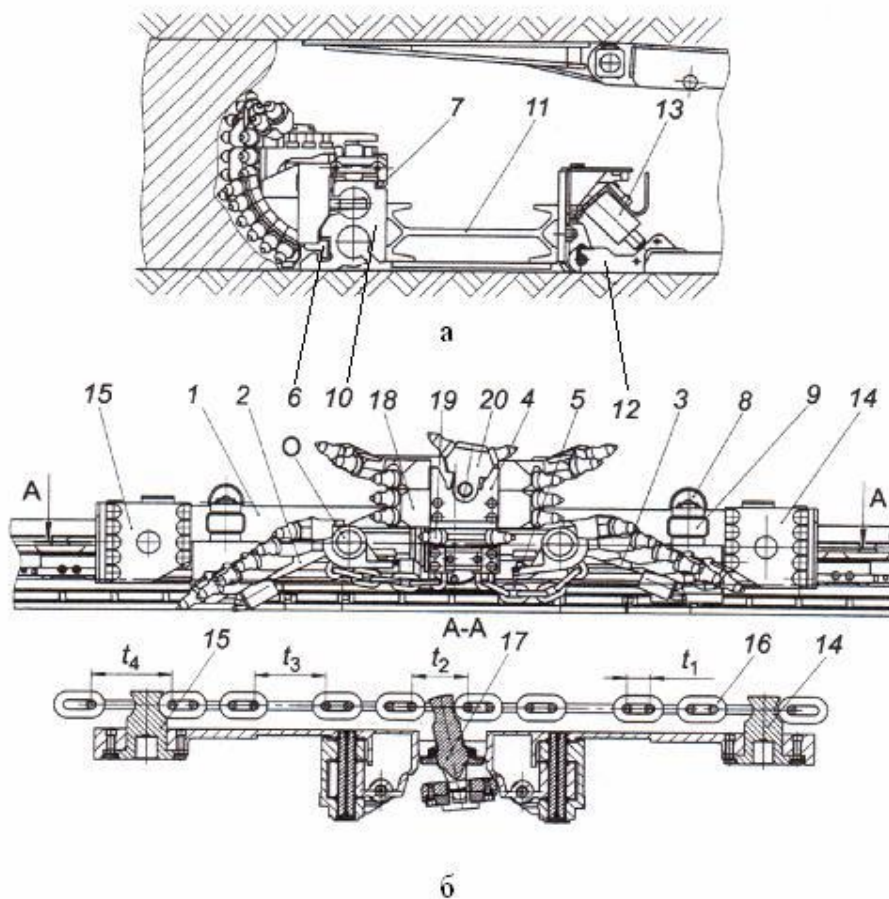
Стругова установка С700: а – вид збоку; б – вид зверху
